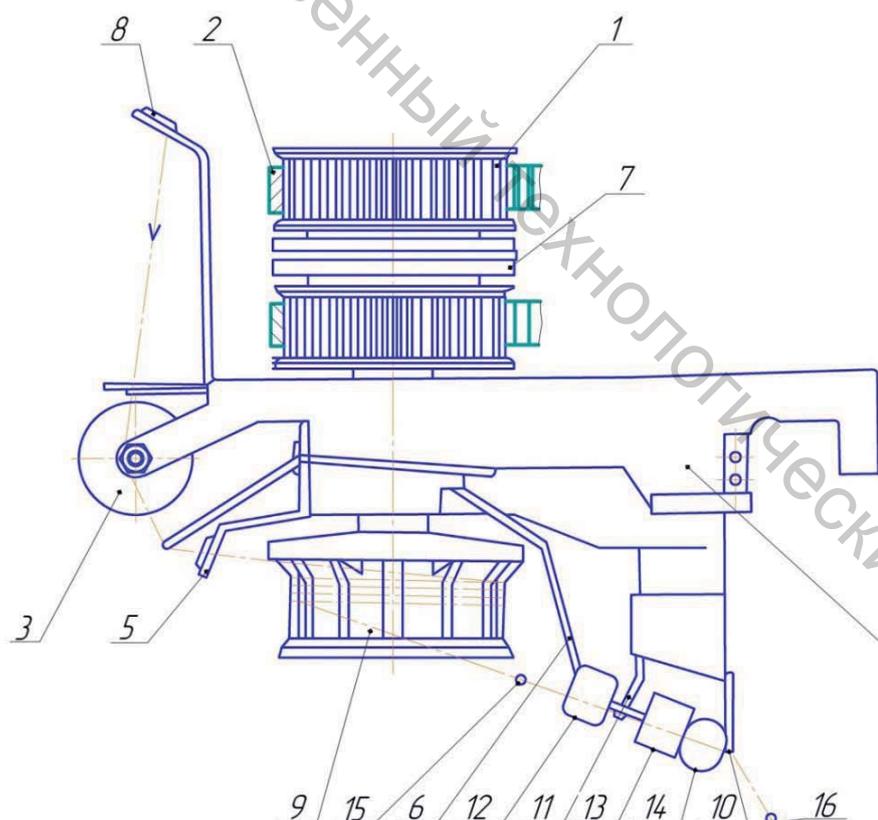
Модернизированная конструкция механизма нитеподдачи
